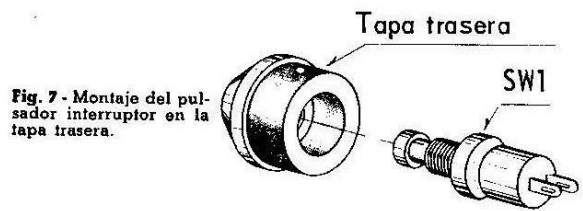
Montaje del pulsador interruptor en la tapa trasera.
